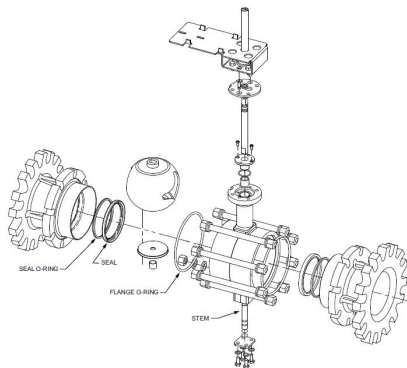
Flanschkgelventil, Explosionsdarstellung
